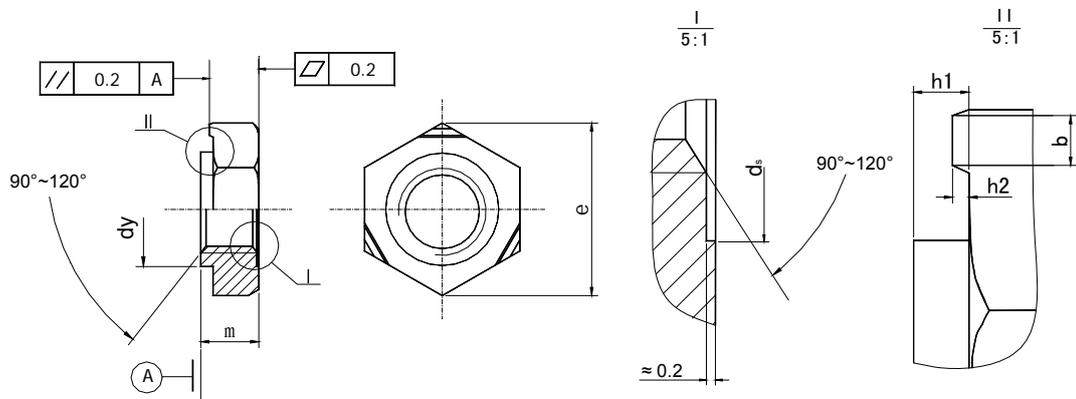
焊接六角螺母 GB13681-92 结构型式
